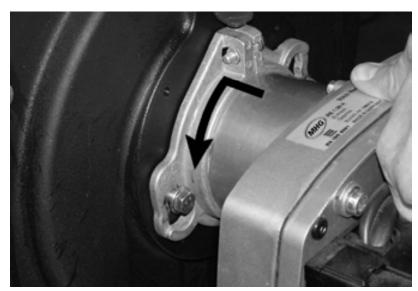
Den Brenner in die Kesseltür einführen, so dass die Brennerbefestigungsschrauben durch den Klemmflansch hindurch stehen. Anschließend den Brenner links herum drehen und danach die Schrauben festziehen.
